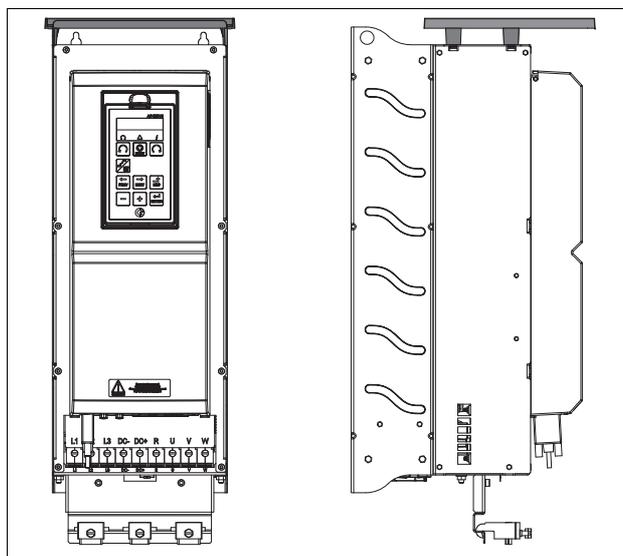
Дополнительная верхняя крышка, установленная на корпусе размера D2
